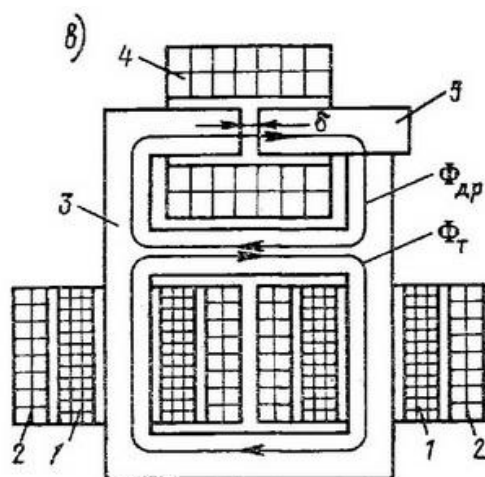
Сварочный трансформатор с воздушным зазором и подвижным ярмом магнитной цепи 5.
